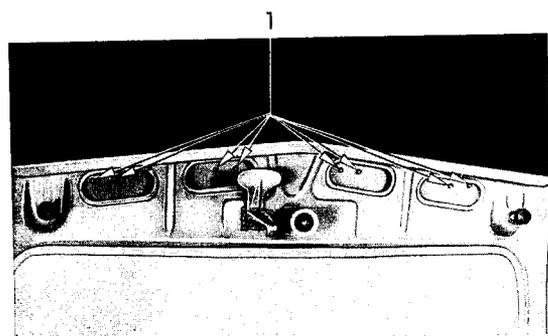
Lage der Federmuttern für Buchstaben auf Haube
